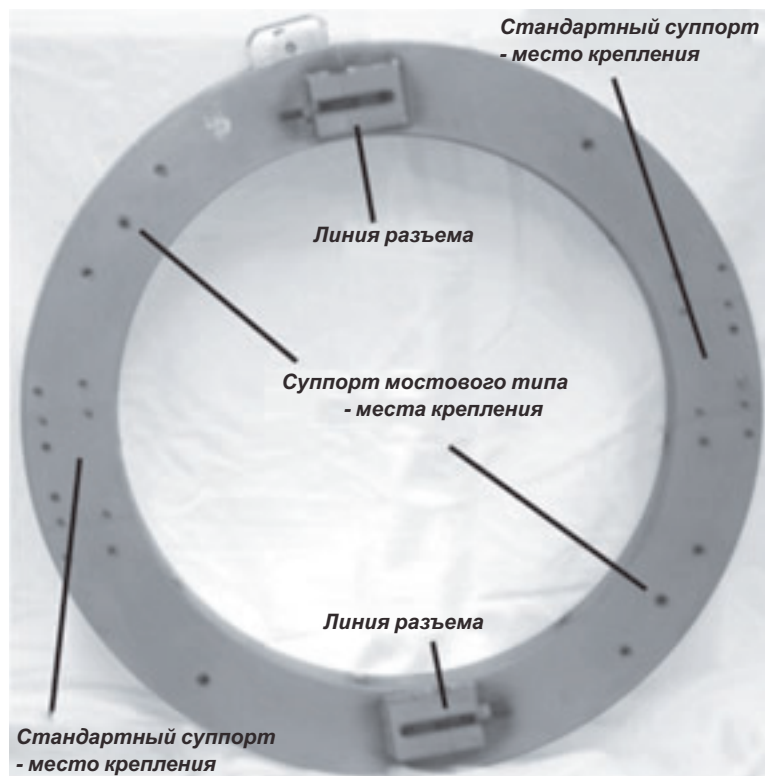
Фотография крепежных отверстий низкопрофильного разъёмного агрегата для суппорта мостового типа. (Различные размеры кольца имеют слегка отличающийся порядок расположения отверстий).
